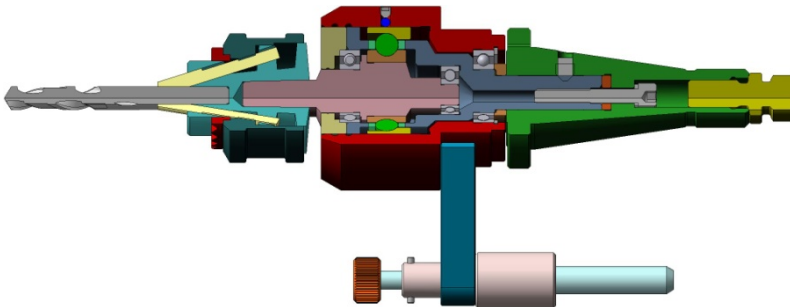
Переріз швидкохідної свердлильної голівки
